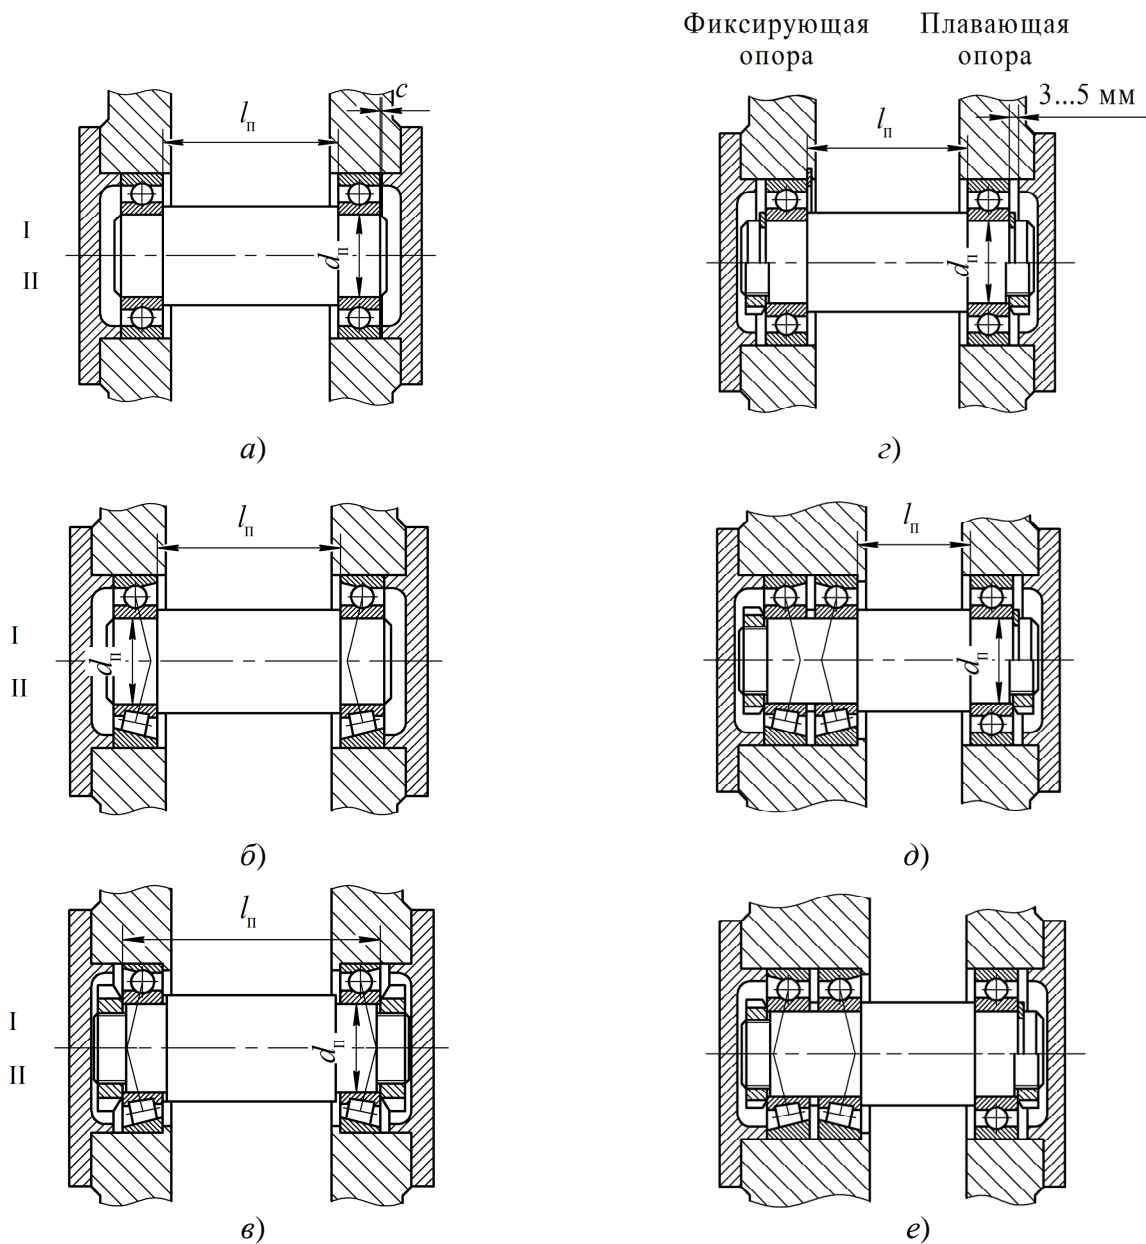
Принципиальные схемы установки подшипников и их фиксирование на валах и корпусе (б, д – схемы «враспор»; в, е – схемы «врастяжку»)
